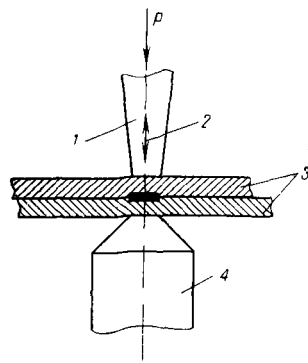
Схема ультразвуковой сварки пластмасс:
